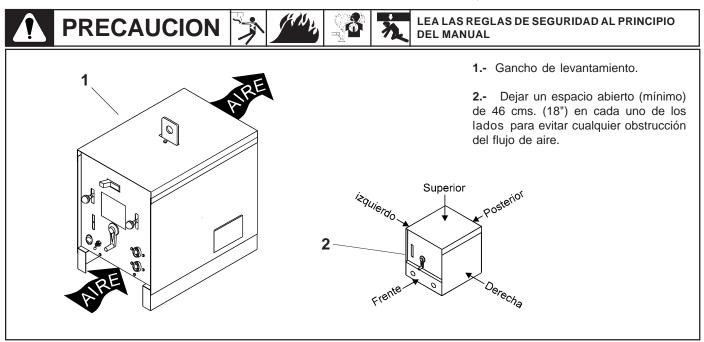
Localización y Movimiento de la Máquina Soldadora.
